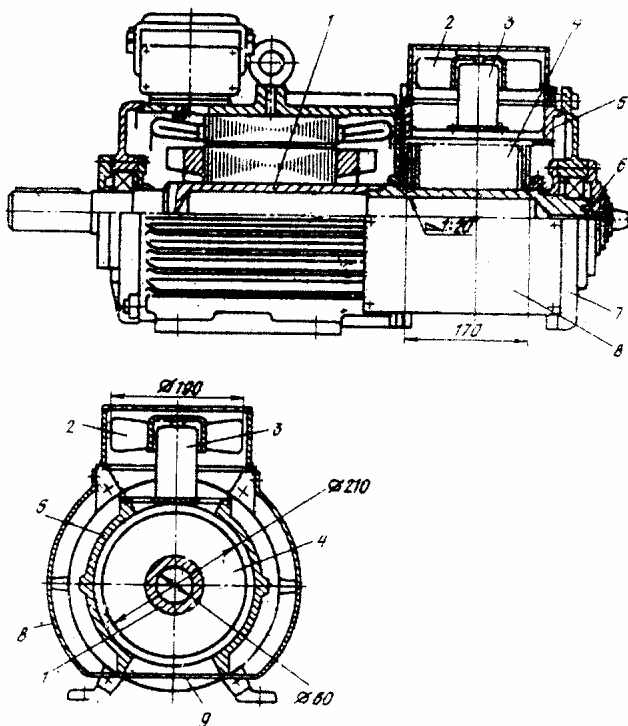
Регулируемый асинхронный электродвигатель с высотой оси вращения 160 мм (мощность 1,1-22 кВт): 1 – вал-тепловая труба; 2 – вентилятор-наездник; 3 – привод вентилятора; 4 – радиатор; 5 – вставка; 6 – штенгель; 7 – подшипниковый щит; 8 – кожух; 9 – окно для выхода воздуха.
